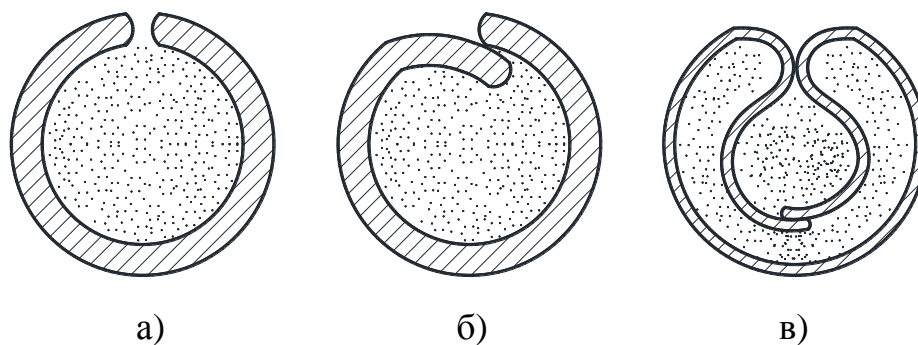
Конструкции поперечных сечений порошковых проволок согласно ГОСТ 26101-84: а – трубчатая стыковая; б – трубчатая с нахлестом кромки; в – двухслойная
